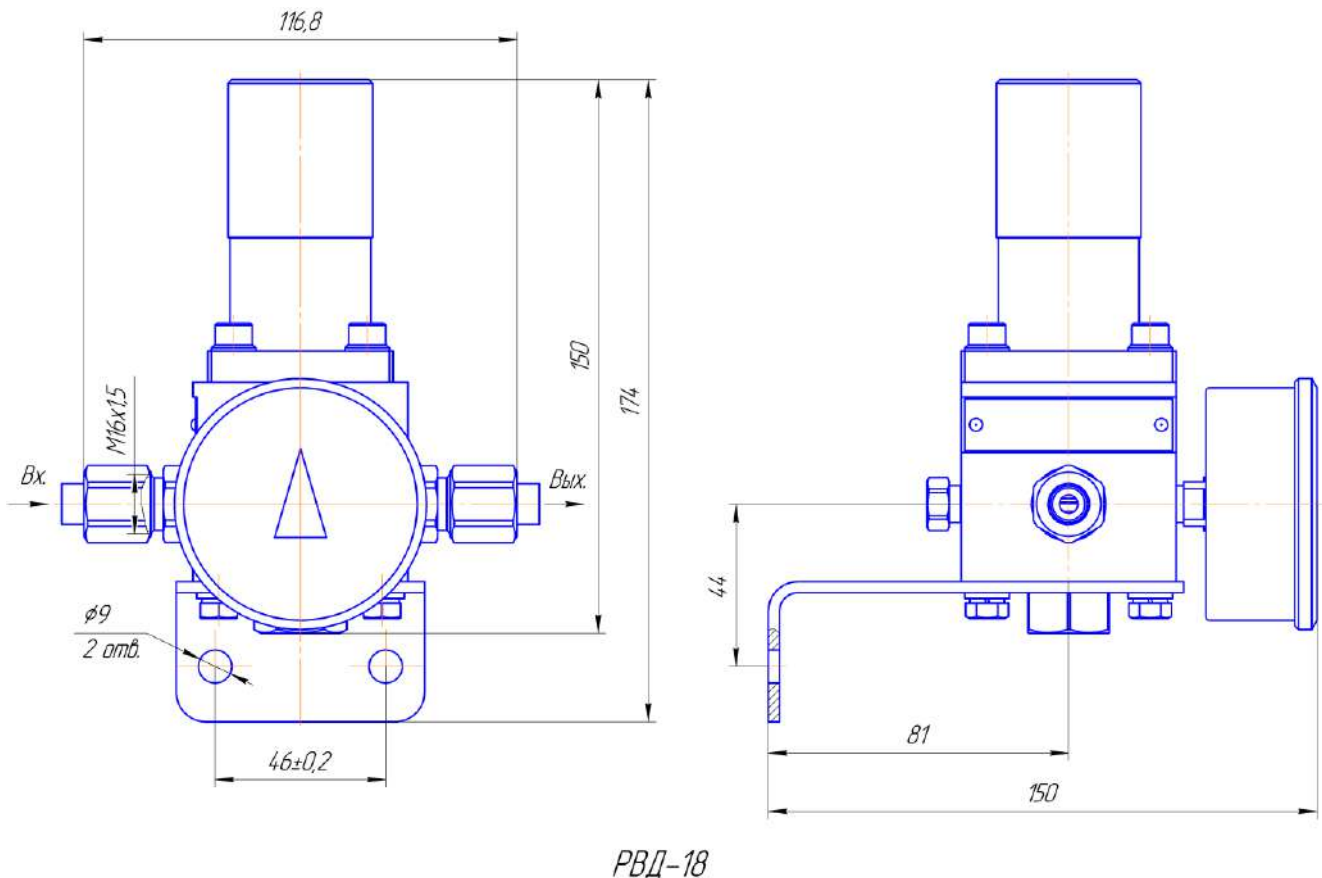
Габаритные и присоединительные размеры редуктора РВД-18
